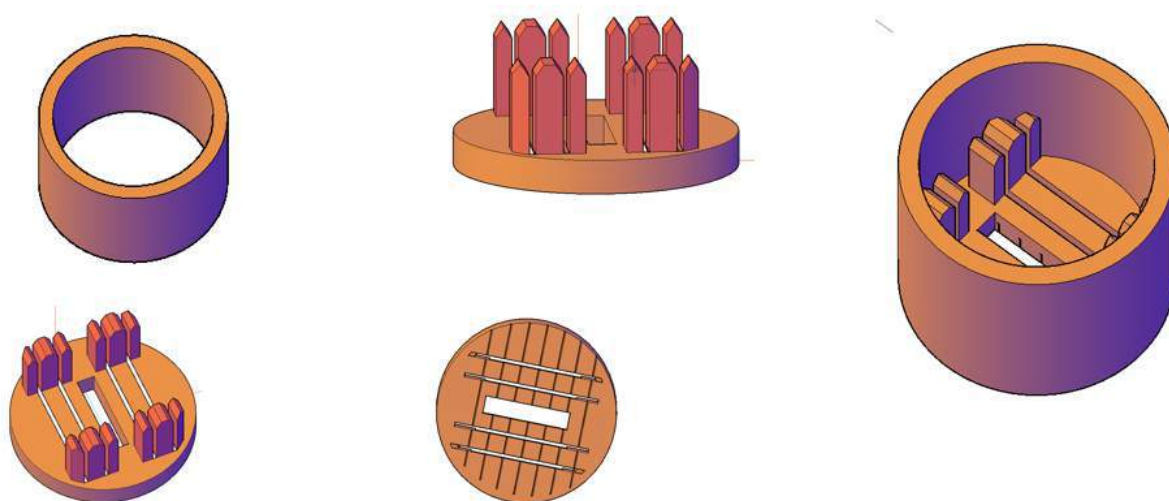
Конструкция основания для фиксации и заливки образцов под шлифовально-полировальное устройство Struers Tegramin-25
